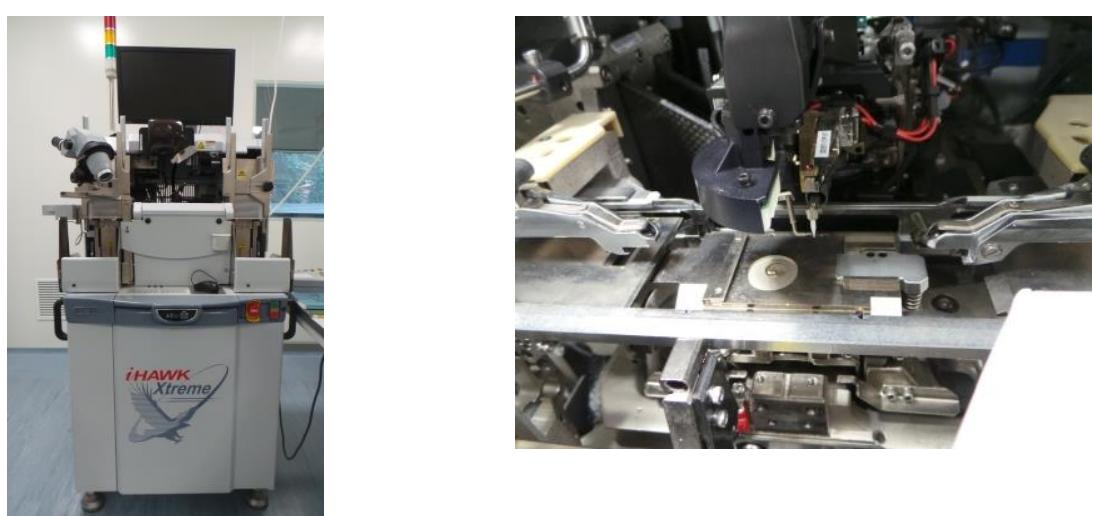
Фото установки сварки проволочных контактов iHawk
